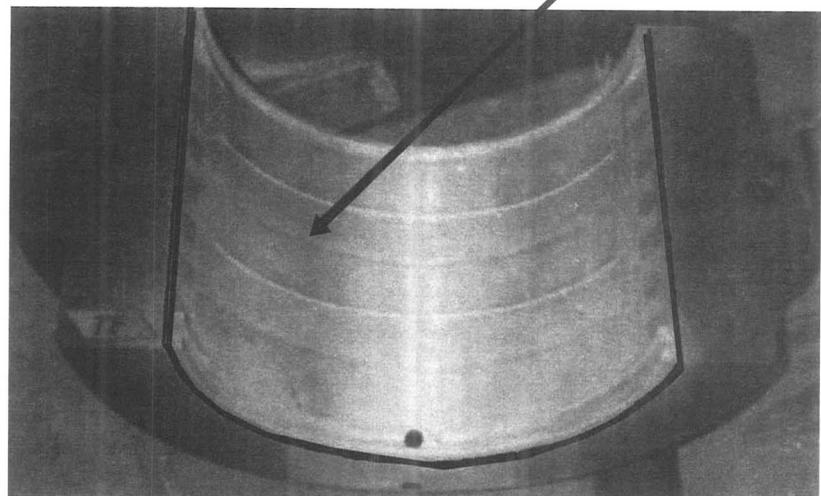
แบริ่งกันรุน (thrust bearing)
